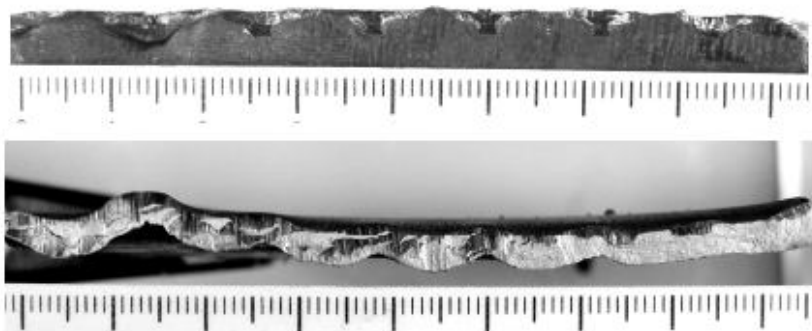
След перерезания металлической пластины, образованный комбинированными ножницами КНР-70 (для экспериментальной резки использовался лист стали марки Ст. 3 толщиной 4 мм, вверху – верхняя поверхность пластины, внизу – торцевая поверхность пластины)
